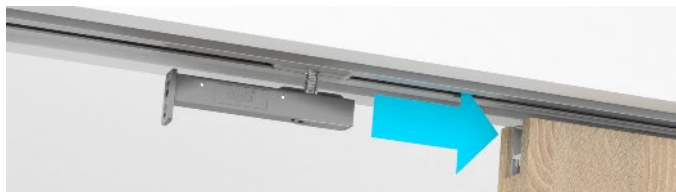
Aufhängung und Schiene mit Schraube 4x18 verschrauben.
